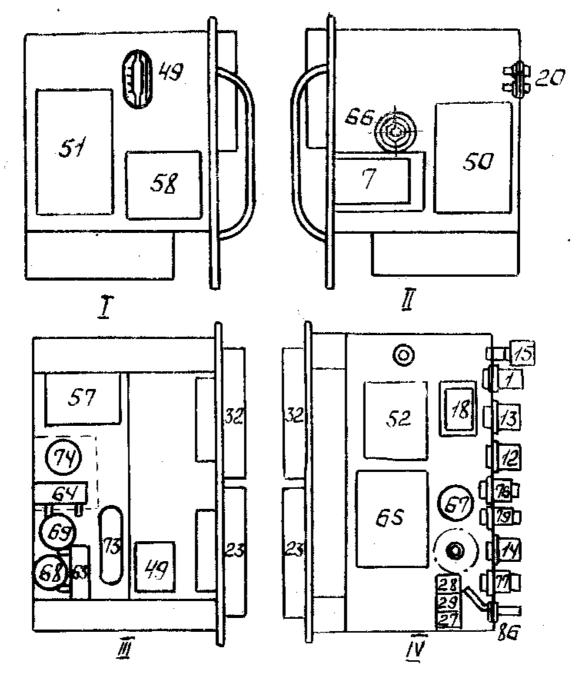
Карта расположения основных элементов измерительного блока вакуумметра ВИТ-2 (ВИТ-2-П): 1 — вид слева; II — вид справа; III — вид сверху; IV — вид снизу.
